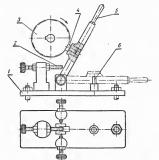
Приспособление для фрезерования шлиц в головках винтов:
